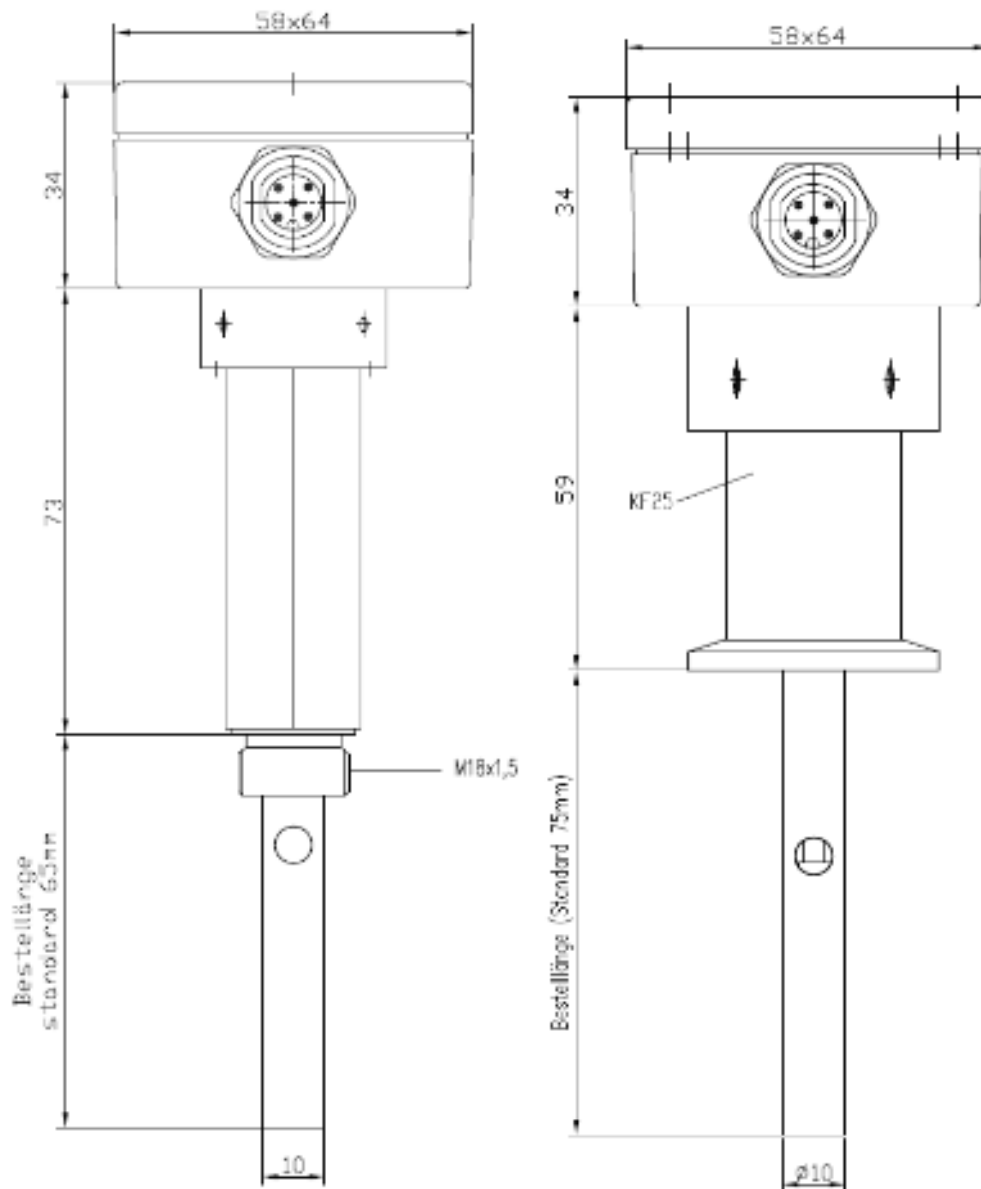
Maßzeichnung Sonde mit Einschraubgewinde (links) und Flansch rechts)
